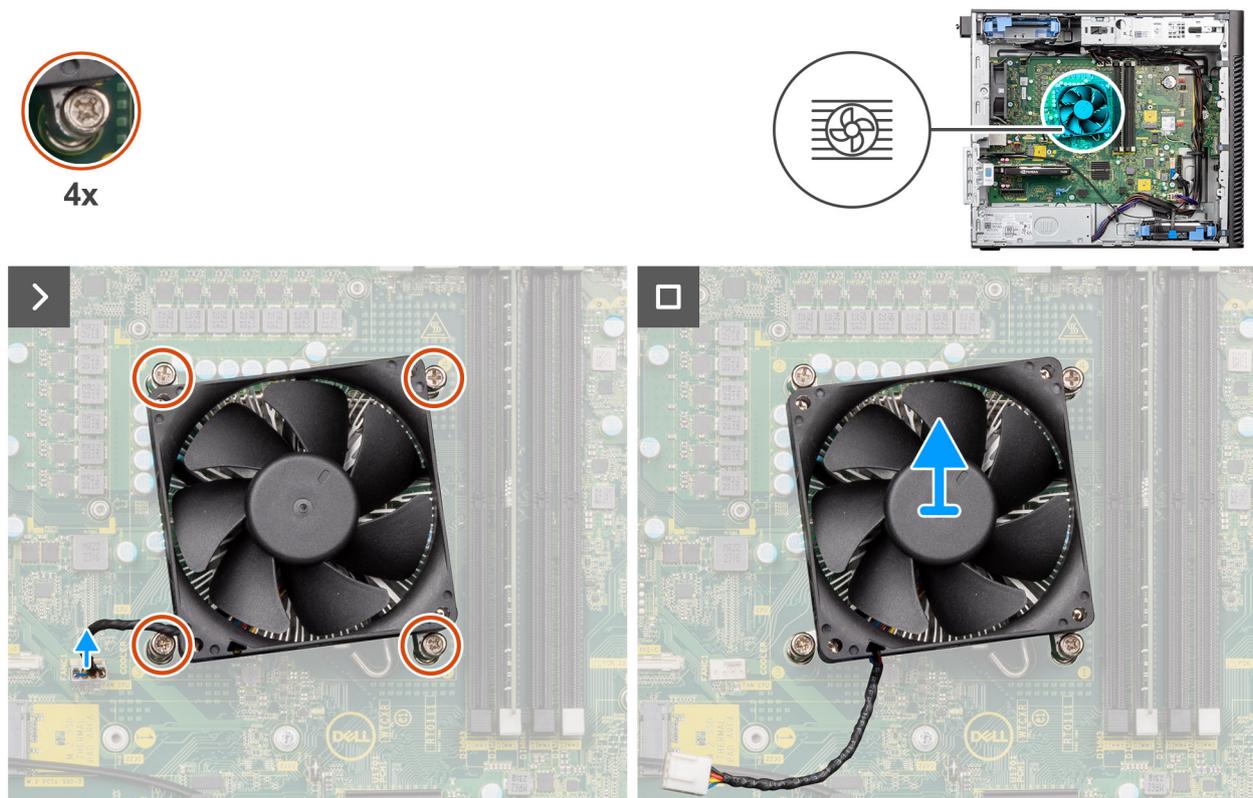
Entfernen des Prozessorlüfters und der 65-W-Kühlkörperbaugruppe
